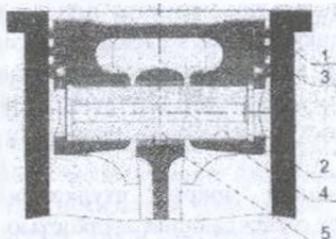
Пары трения: 1 - втулка - поршневые кольца; 2 - втулка - юбка поршня; 3 - канавки поршня - поршневые кольца; 4 - бобышки поршня - поршневой палец; 5 - поршневой палец - поршневая головка шатуна.
